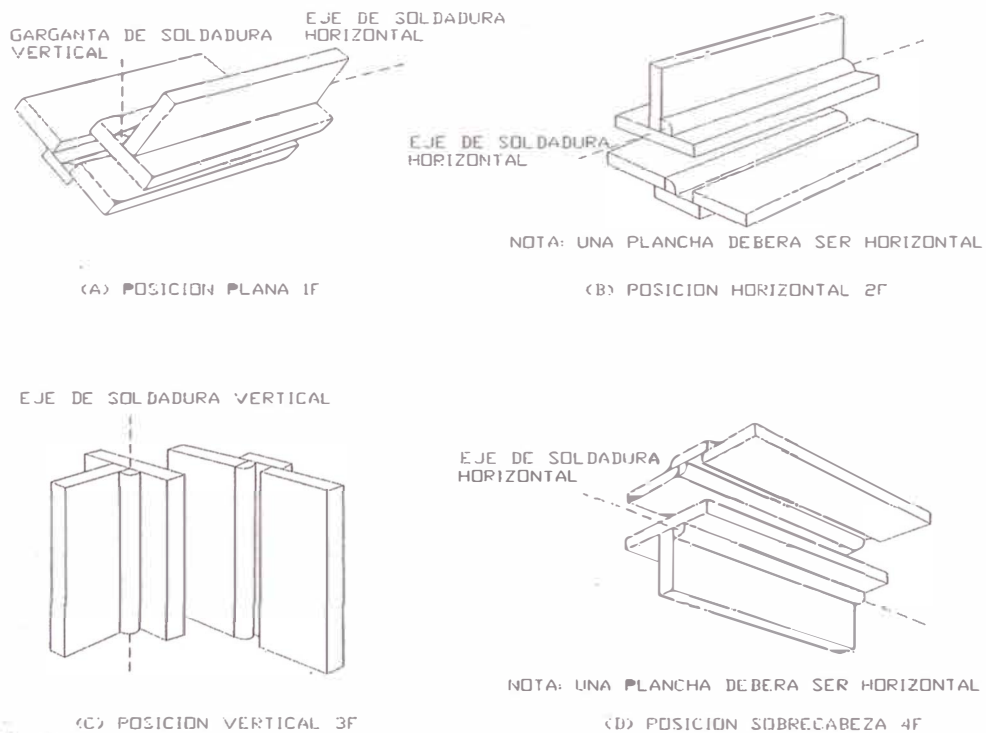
posiciones de prueba en planchas – Juntas de Filete
